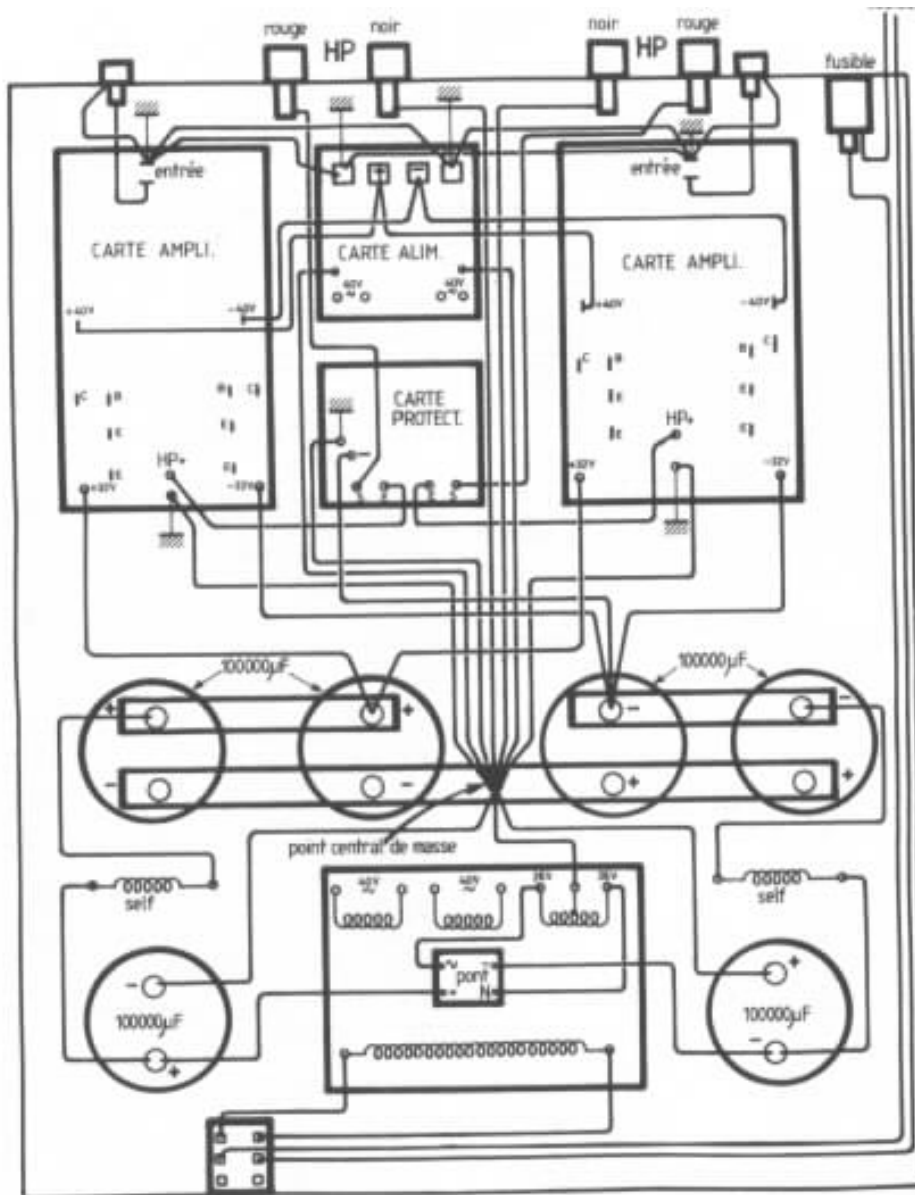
Plan de câblage. On notera le point de masse central illustré sur les photos ci-contre.
